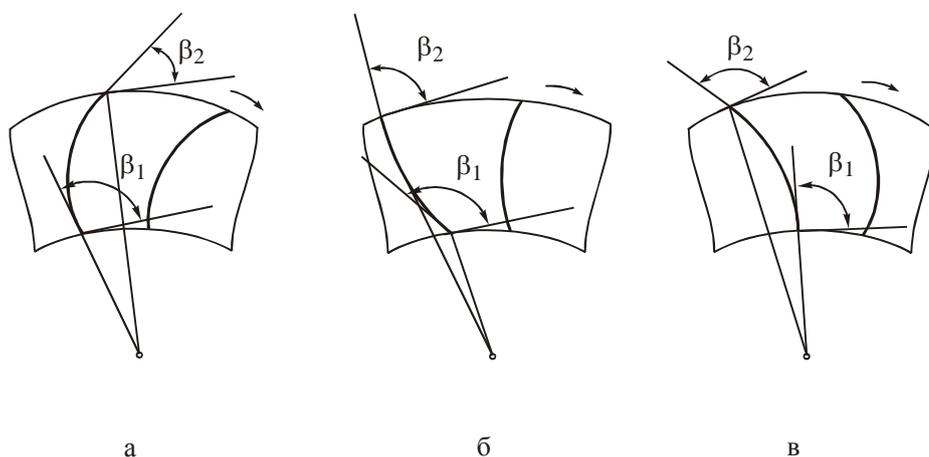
Форма лопаток рабочего колеса вентилятора:
